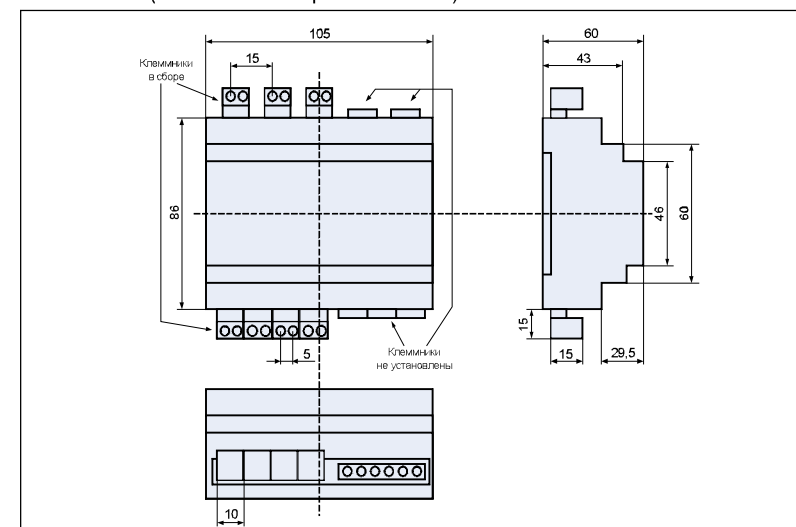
Габаритные размеры корпуса четырехканального диммера (каталожные номера 00150...00199)
